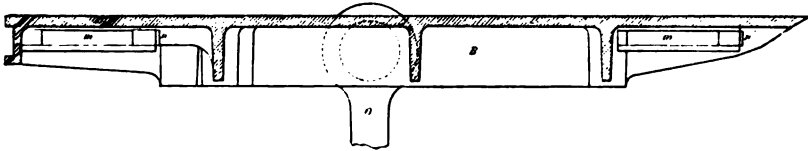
Coupe longitudinale des planchers supérieurs du cadre n° III.
